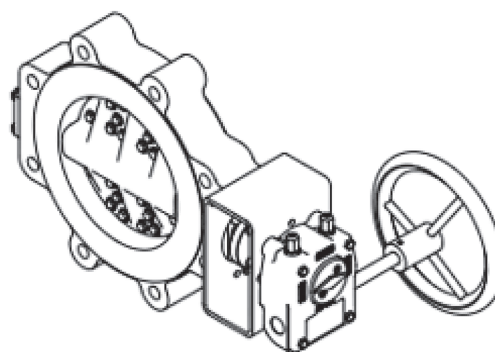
Posiciones de montaje del actuador Rotork (CP/GP)
